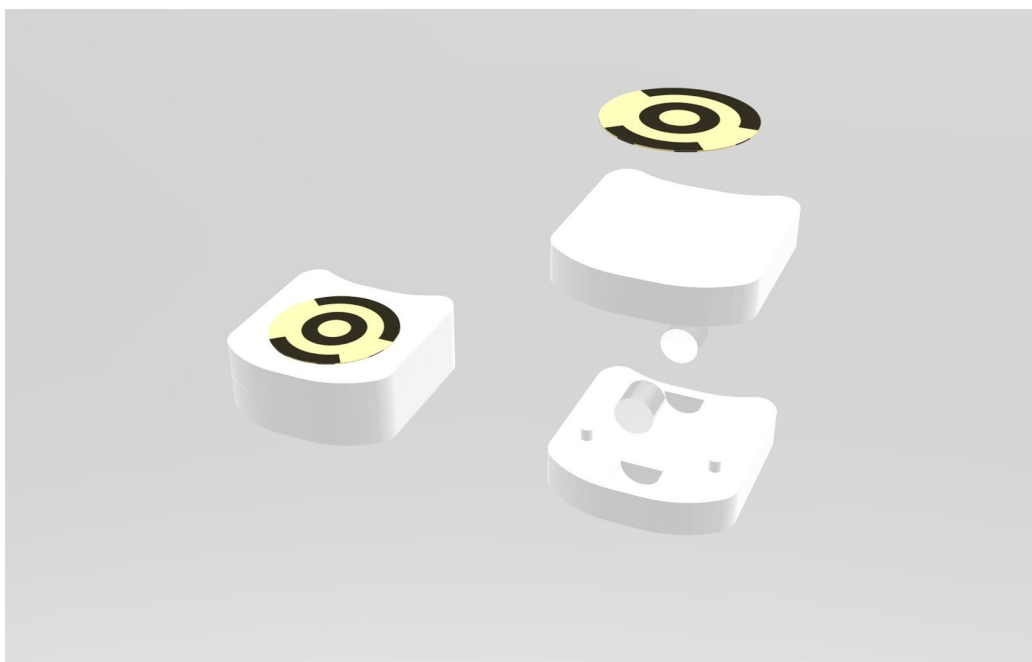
Manipulable ensamblado (izquierda) y explosión (derecha).
